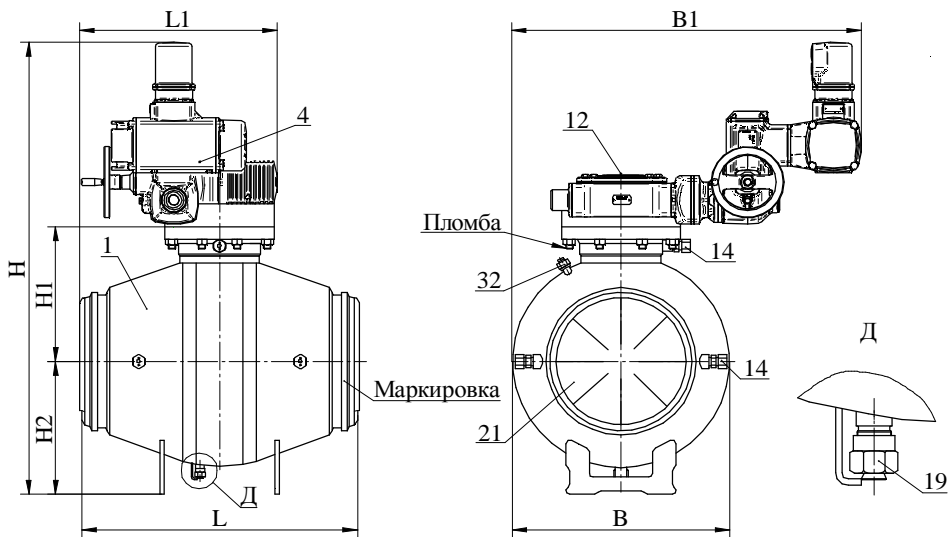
Кран шаровой надземной установки с электроприводом
